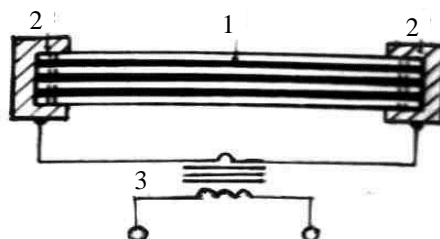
Пакет пластин, сваренных диффузионной сваркой
